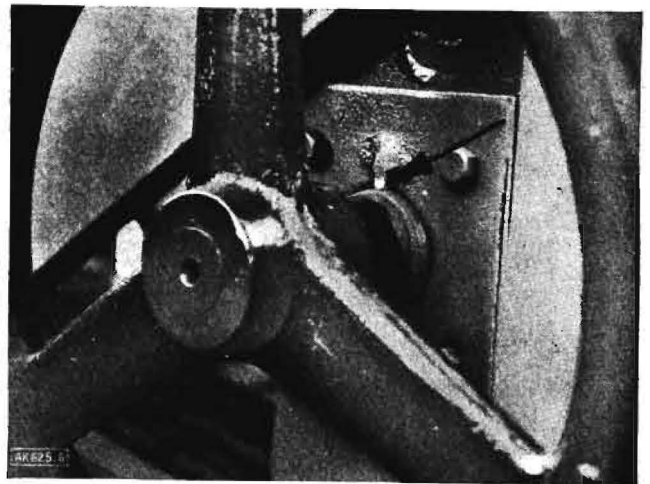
Kurbelwellenhauptlager. Aufnahme der Buchse mit balligem Ring in gelochter Blechplatte und mit Sicherungsstift
